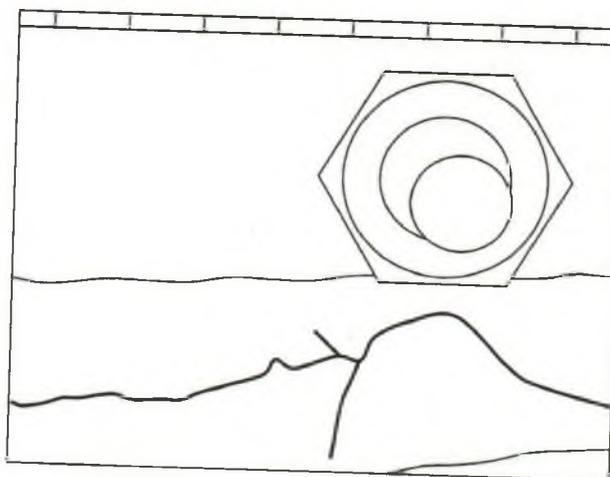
Разветвленная трещина нахлесточного сварного соединения. Общий вид
